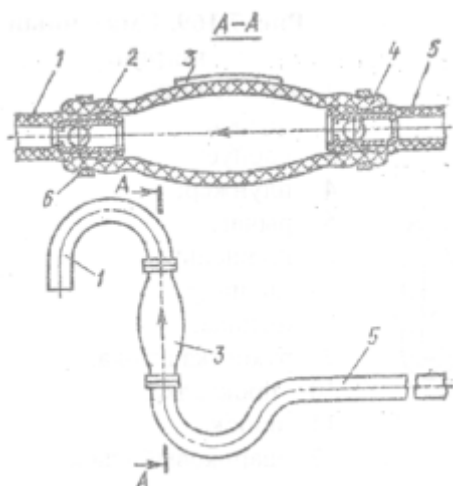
Насос для ручной перекачки топлива: 1 - короткий шланг; 2, 4 - шарики соответственно нагнетательного и всасывающего клапанов; 3 - корпус; 5 - длинный шланг; 6 - хомуты.
